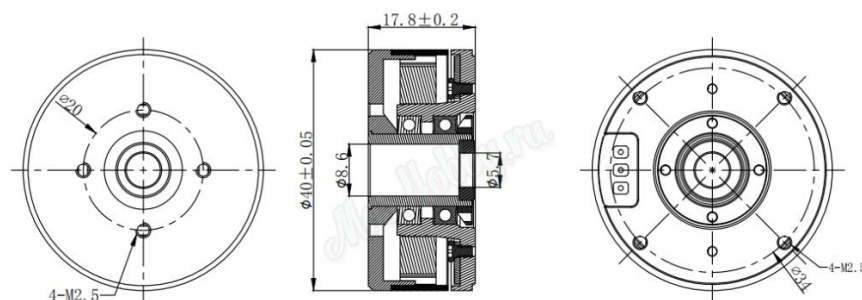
Конструкція сервомотору GM3506 [57]
